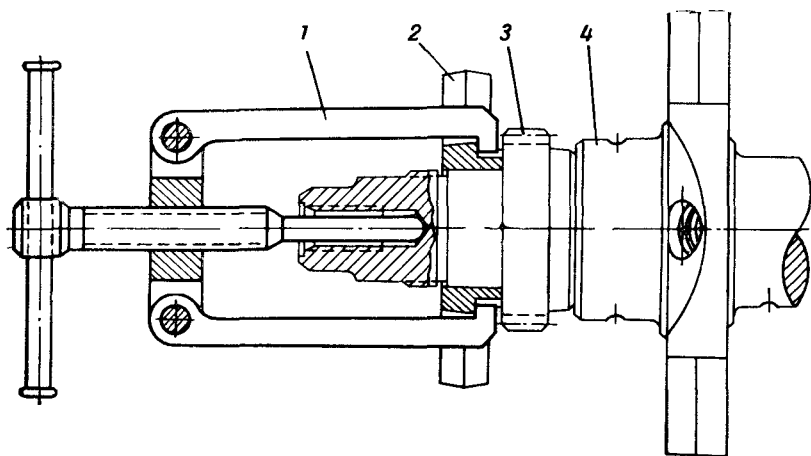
Снятие переднего противовеса и шестерни коленчатого вала:
